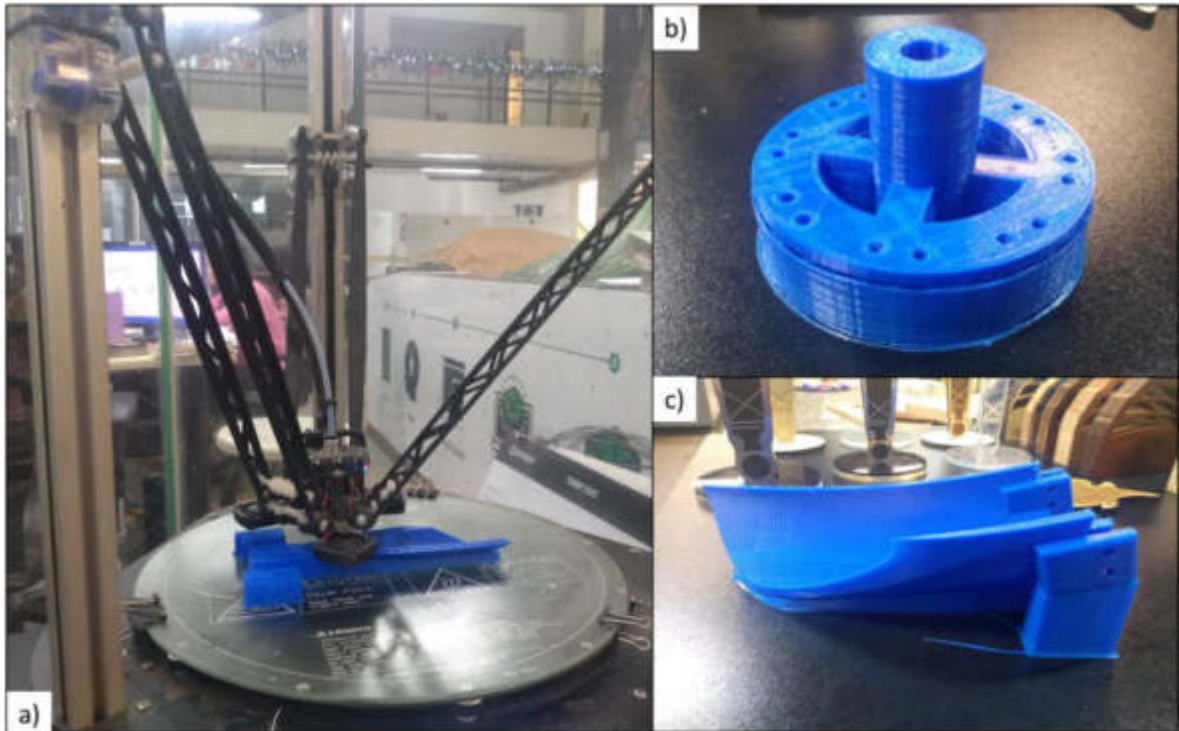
Manufactura de la turbina mediante impresión 3D: a) Impresión de álabe, b) Soporte del rodete, c) Álabe de la turbina.
